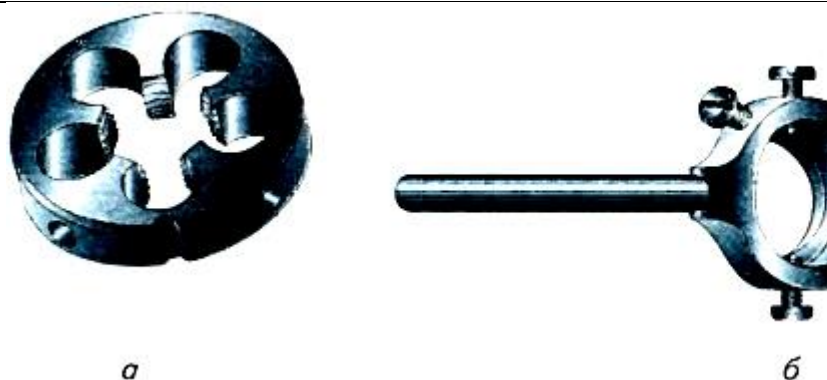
Круглая плашка (а) и плашкодержатель (б)
